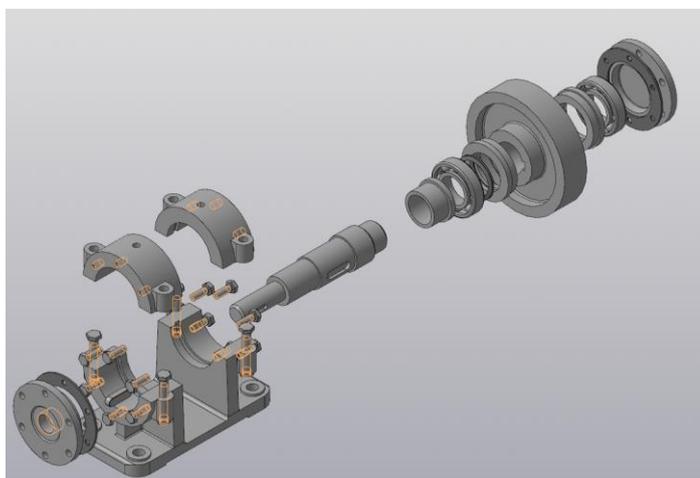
КЭМ деталей сборочного изделия «Ролик поддерживающий»
